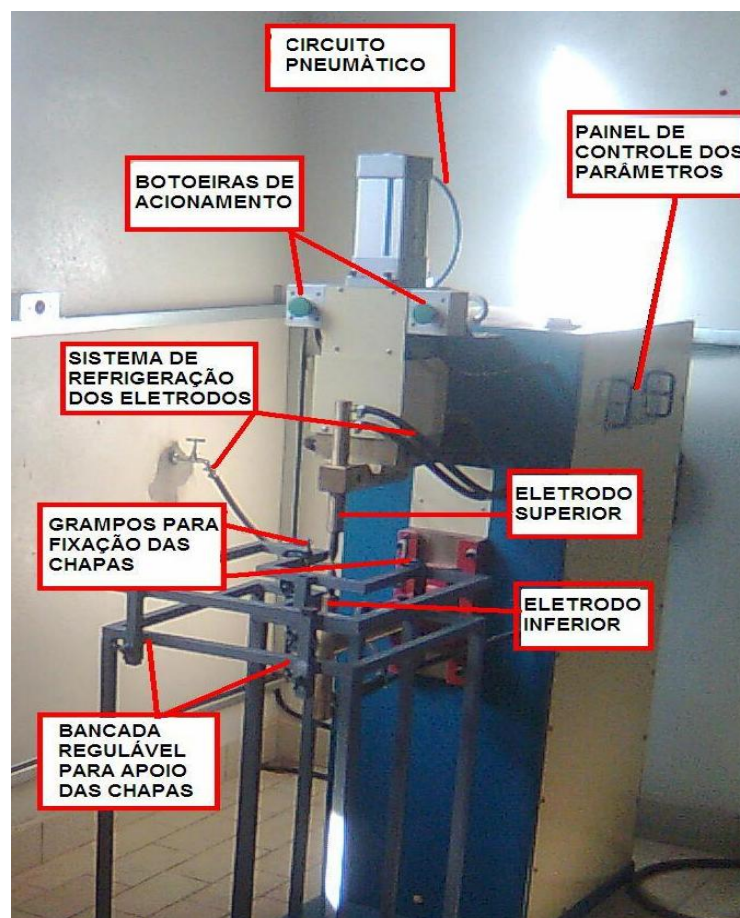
1– Principais componentes da máquina de soldagem a ponto utilizada nos experimentos
